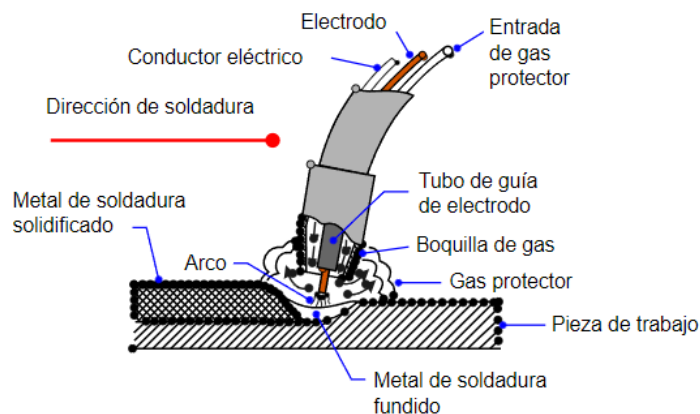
Esquema general del proceso de soldadura GMAW.
